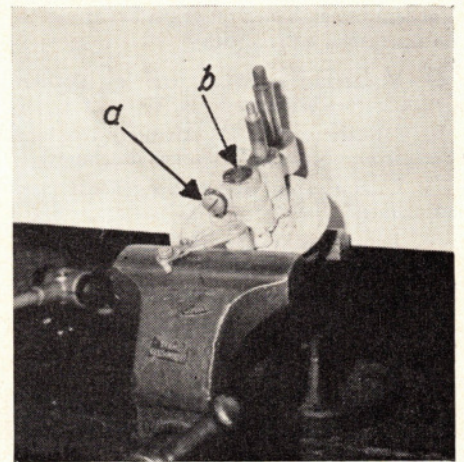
a = Führungsschraube für Tachoritzel, b = Achsmutter.
